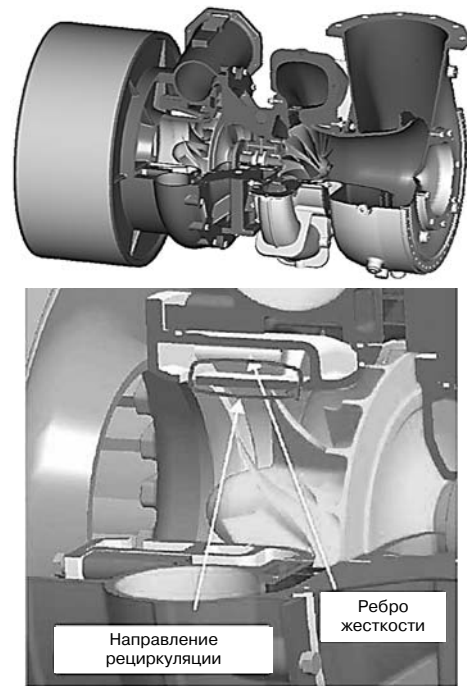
Новый турбокомпрессор TCR с устройством для внутренней рециркуляции (IRC)
